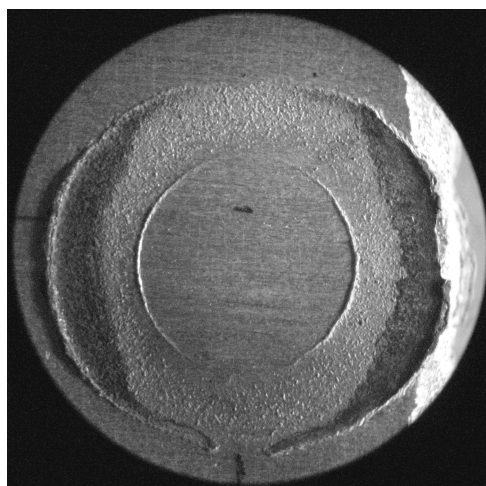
Характерный отпечаток, образовавшийся на поверхности образца-пластины в результате фреттинга ($\times 3$, образец 2.3.0)
